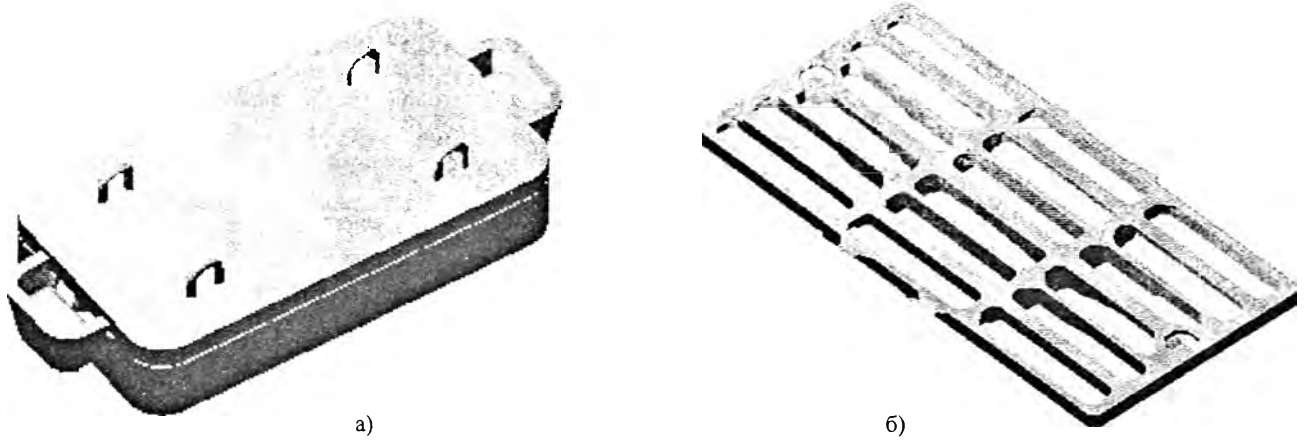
Рассчитываемое пространство отливки "решетка" (б) и кокиля(а)
